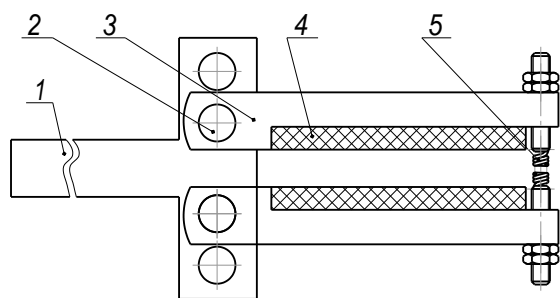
Устройство для чистовой обработки наружных поверхностей профильных деталей
